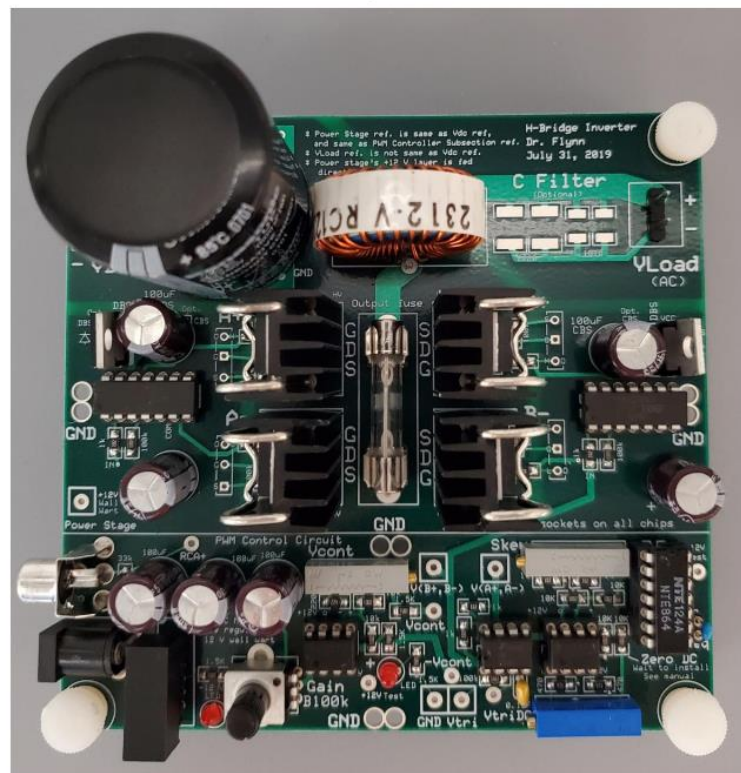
Placa del puente H soldada en el laboratorio
